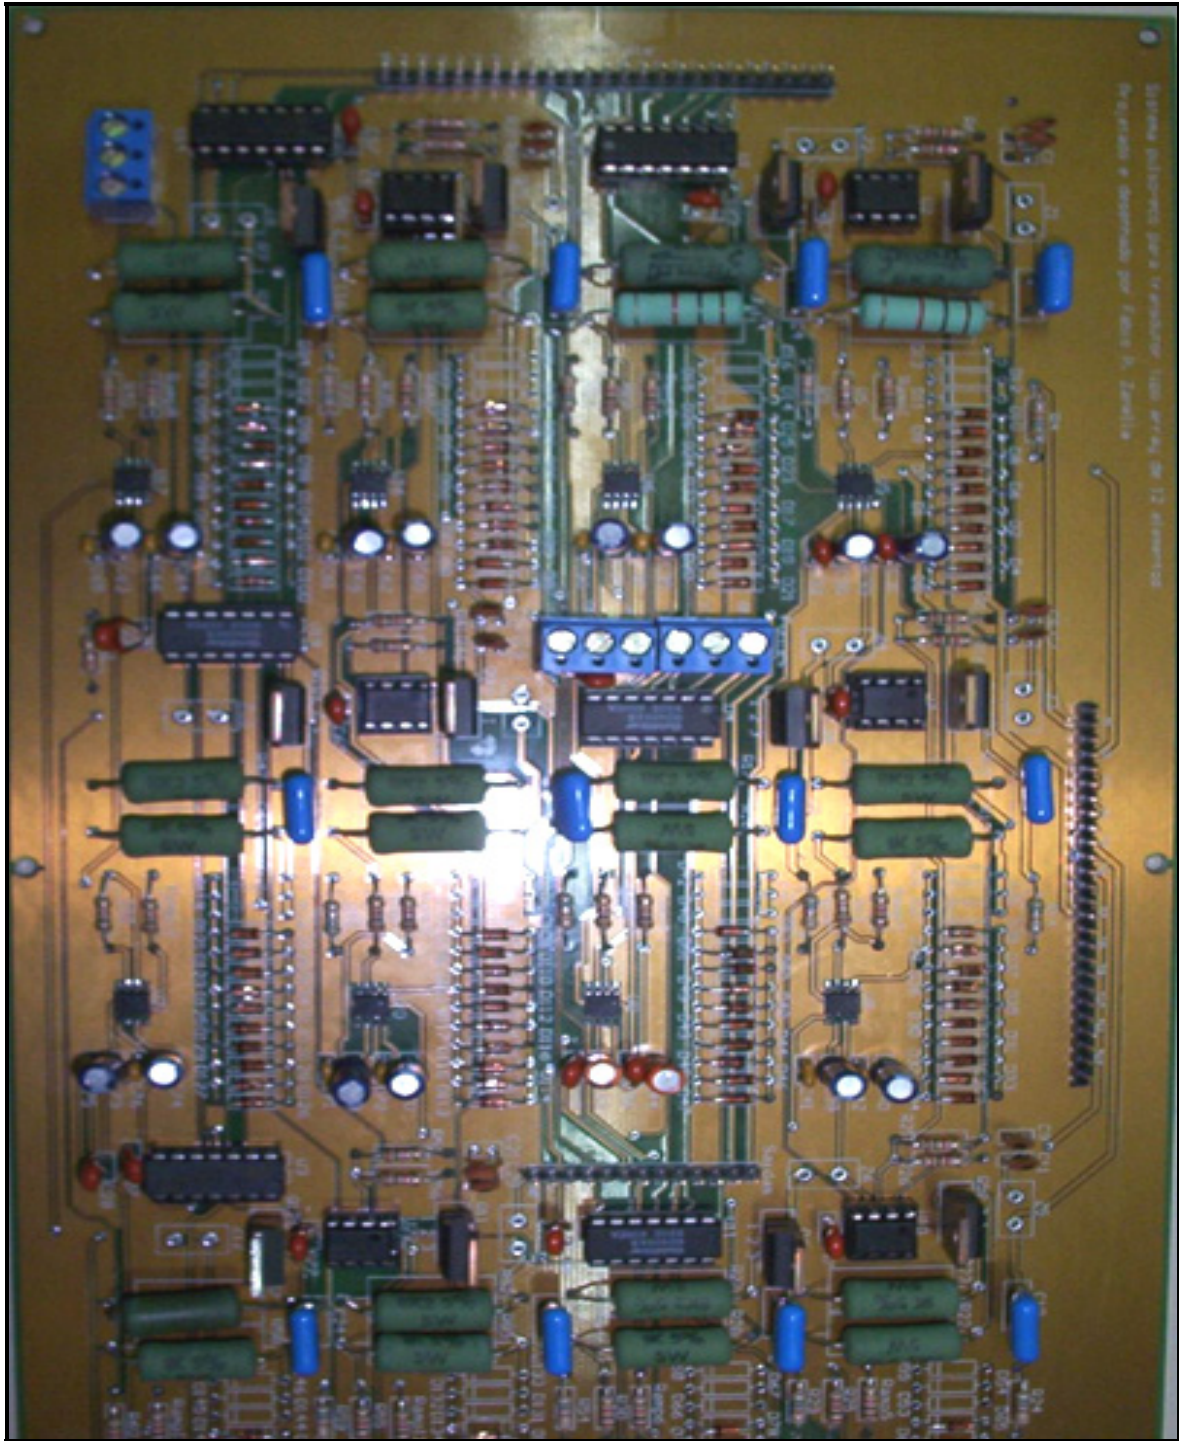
Placa de circuito impresso com os componentes dos 12 canais montados.
